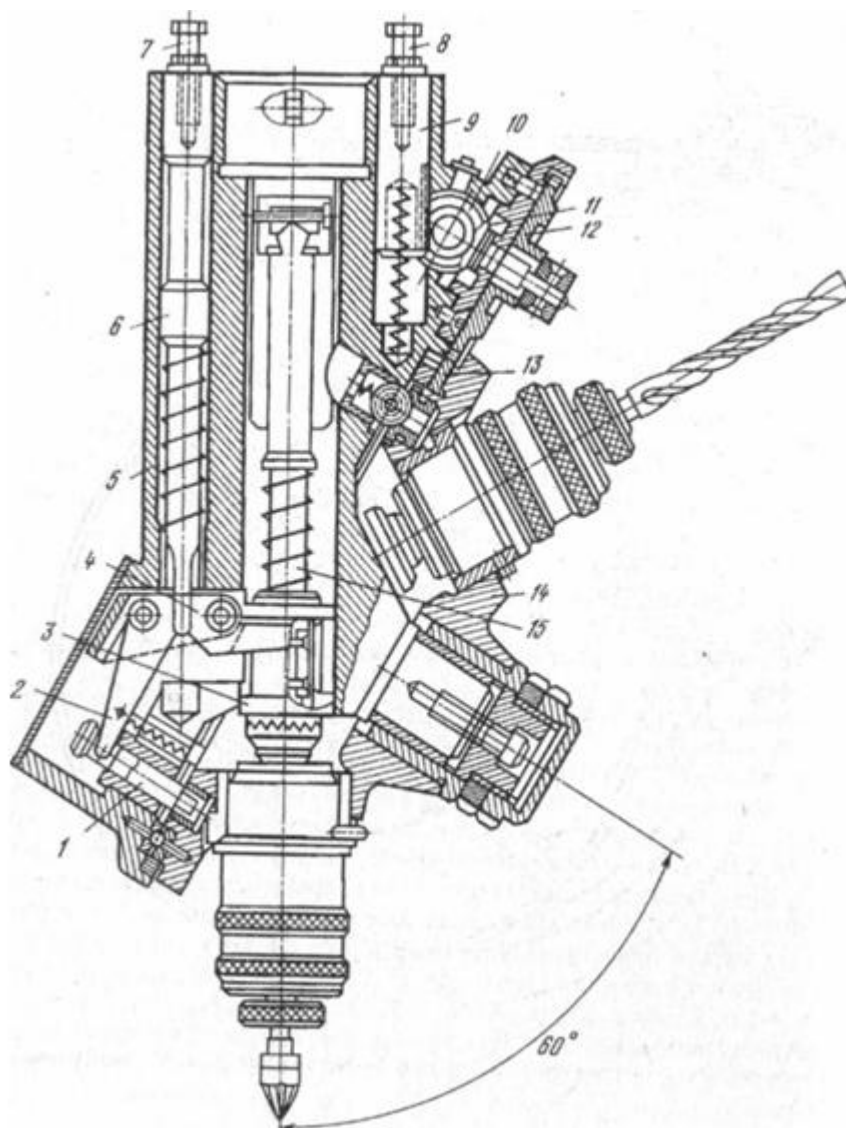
Револьверная шестишпиндельная головка вертикально-сверлильного станка: 1 - фиксатор; 2 - рычаг фиксатора; 3 - ведущая полу-муфта; 4 - рычаг муфты; 5 - корпус основной; 6 - стержень; 7, 8 - упорные винты; 9 - рейка; 10 - зубчатое колесо; 11 - коническая зубчатая передача; 12 - храповой механизм; 13 - зубчатый венец; 14 - поворотный корпус; 15 - ведущий шпиндель головки зубчатый
